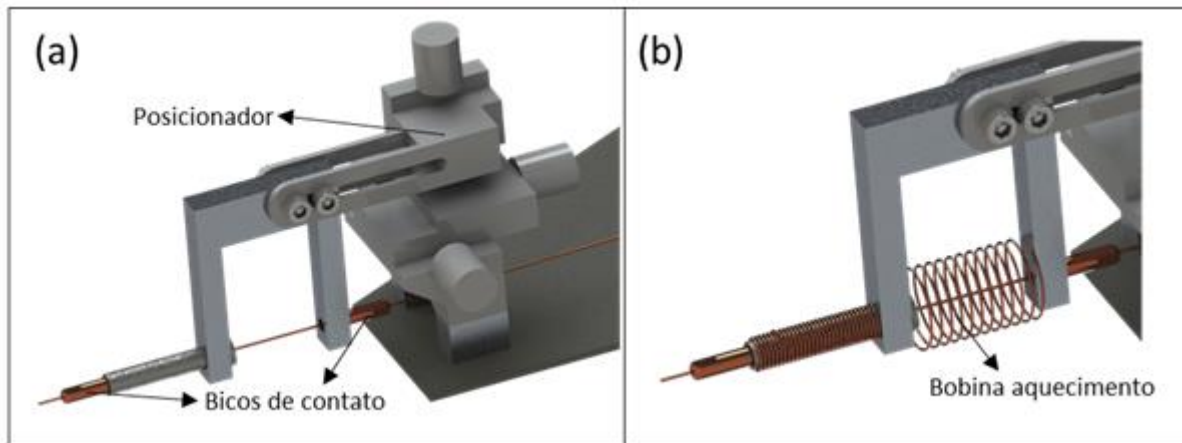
Sistema de ajuste de posição (a) posição da bobina de aquecimento indutivo (b)
